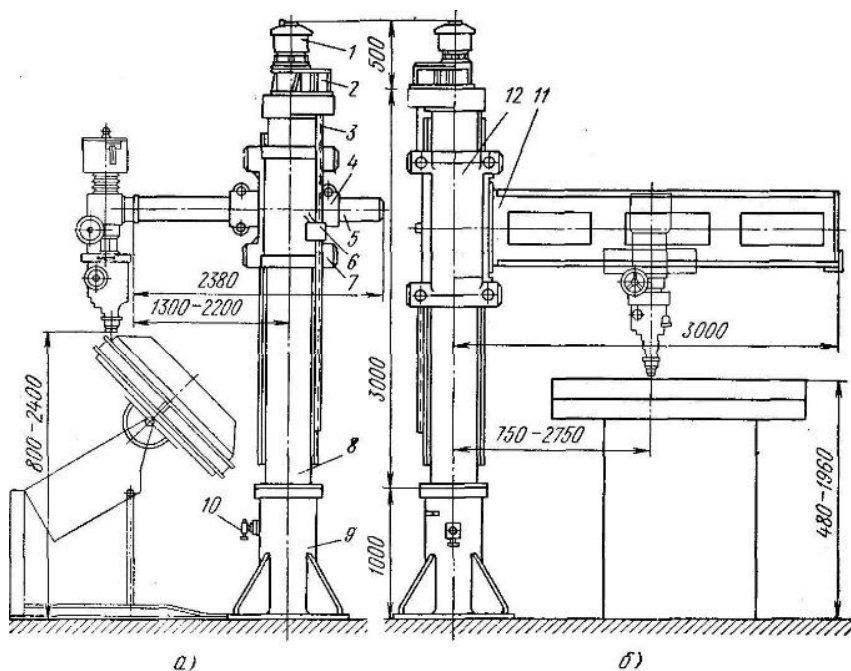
Поворотные колонны ПК-1 для сварочных головок
